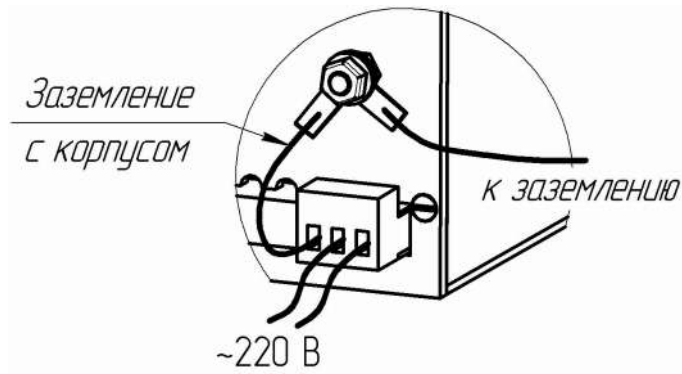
Заземление корпуса ИП щитового исполнения для улучшения ЭМС
